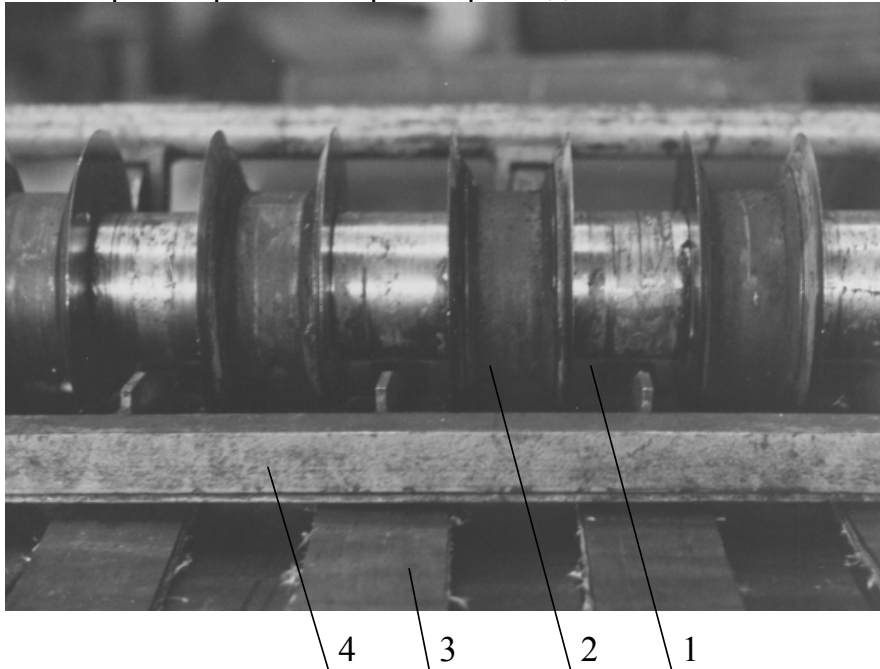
Ножовий блок установки для розрізання конвеєрної стрічки:
